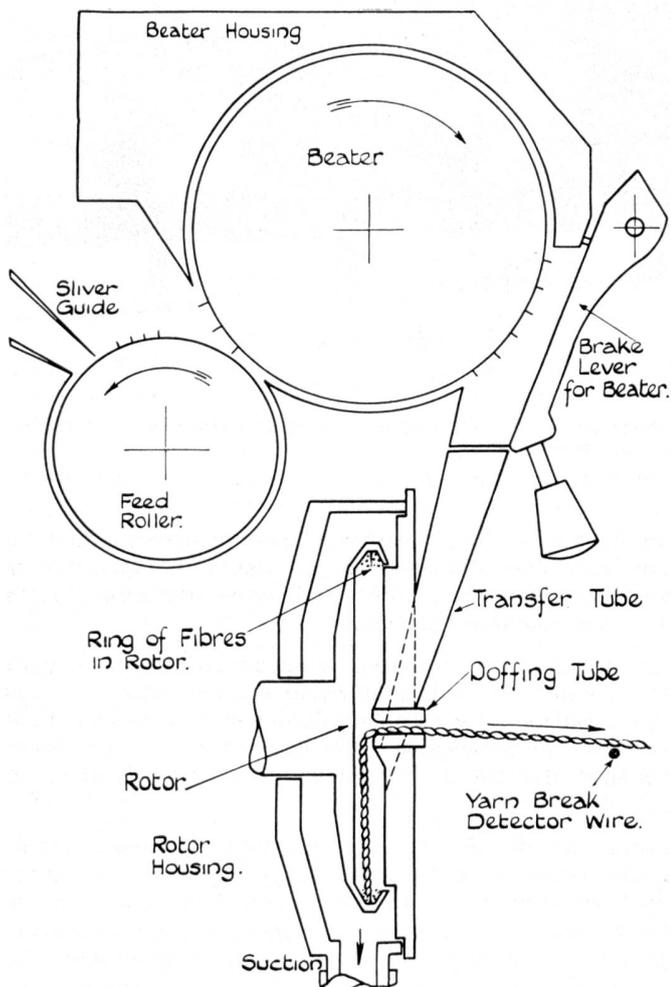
Basisstruktur einer Offen-End-Anlage für Langstapelfasern; beater housing = Gehäuse der Schlagmaschine bzw. des Schlägers; beater = Schlagmaschine bzw. Schläger; sliver guide = unverzogene Bandzuführung; feed roller = Zufuhrwalze; brake lever for beater = Bremshebel für Schlagmaschine bzw. Schläger; ring of fibres in rotor = Faserring im Rotor; transfer tube = Uebergaberohr; rotor = Rotor; rotor housing = Gehäuse des Rotors; suction = Ansaugseite; doffing tube = Fadenspinrohr; yarn break detector wire = Detektordraht zum Feststellen von Garnbrüchen (BFF).
